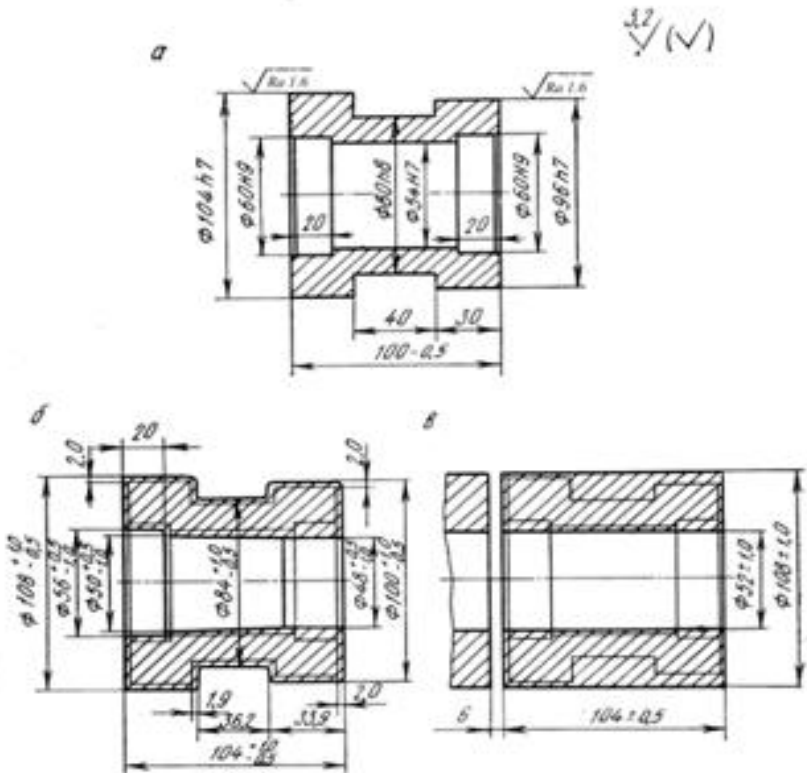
Втулка: а – оброблена деталь; б – штамповка на ГKM; в – заготовка із труби.
